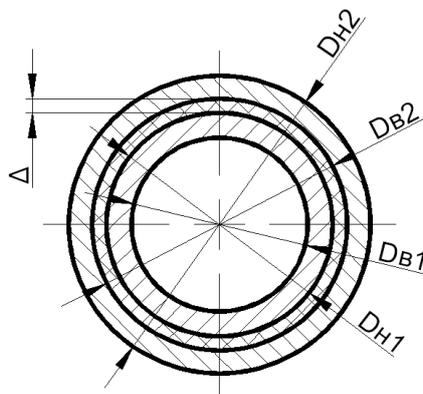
Поперечное сечение двухслойного гидроцилиндра
